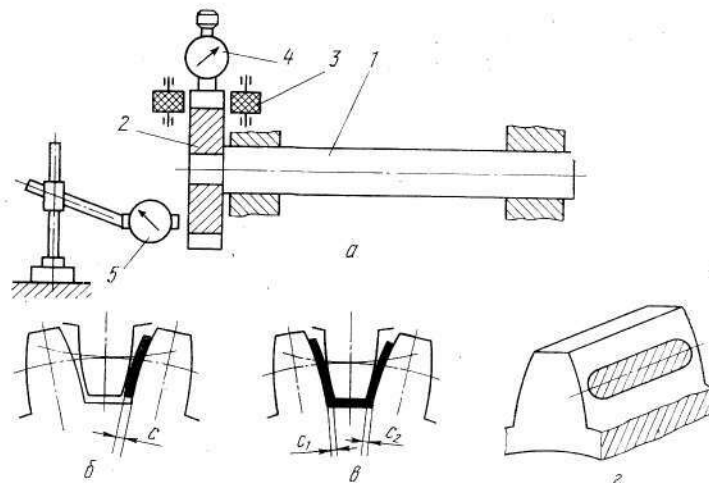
Схема проверки цилиндрических зубчатых передач
